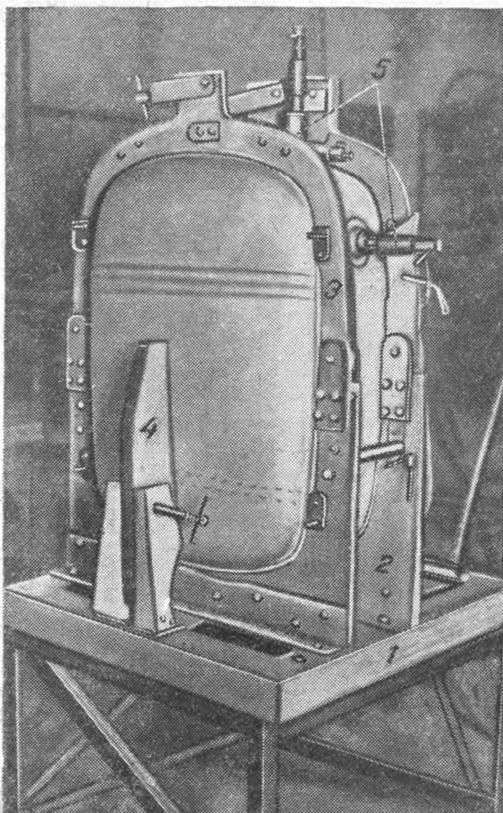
Простая конструкция приспособления для сборки каркаса фонаря.
